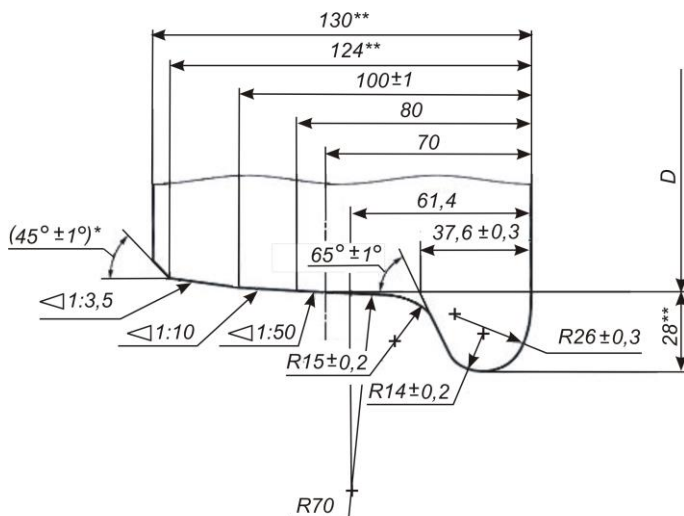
Объединенный профиль поверхности катания колеса
